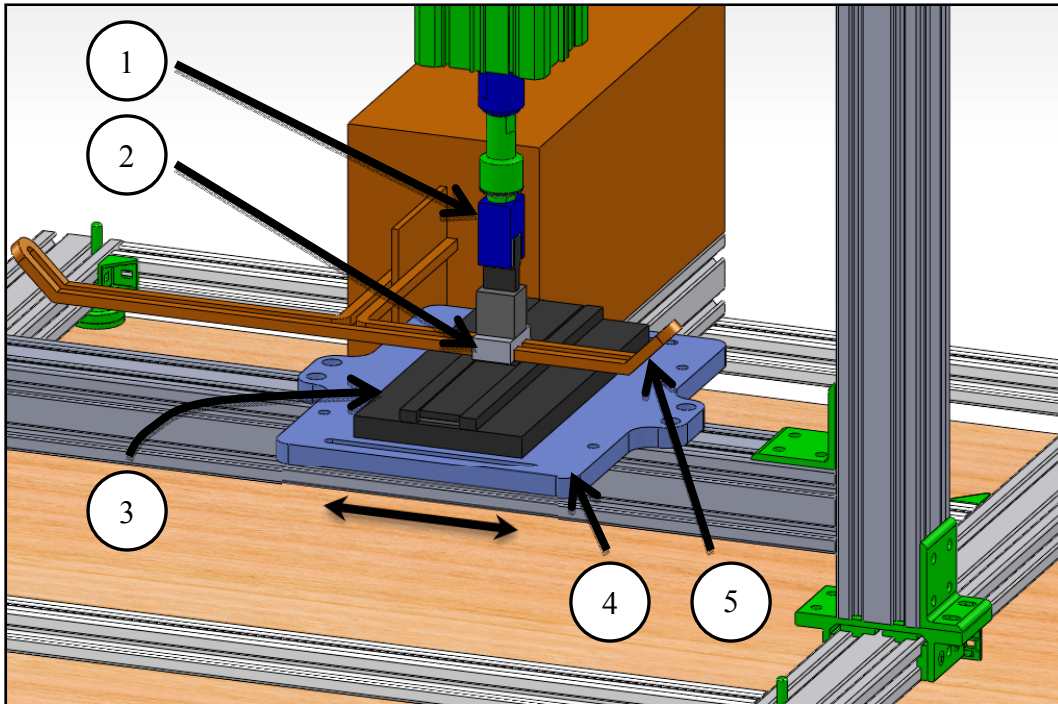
Montage de soudage : vue 3D du détail de la zone de soudage
